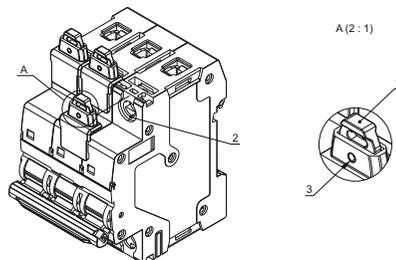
Монтаж заглушки / Figure 5 – Installation of the blanking plug
